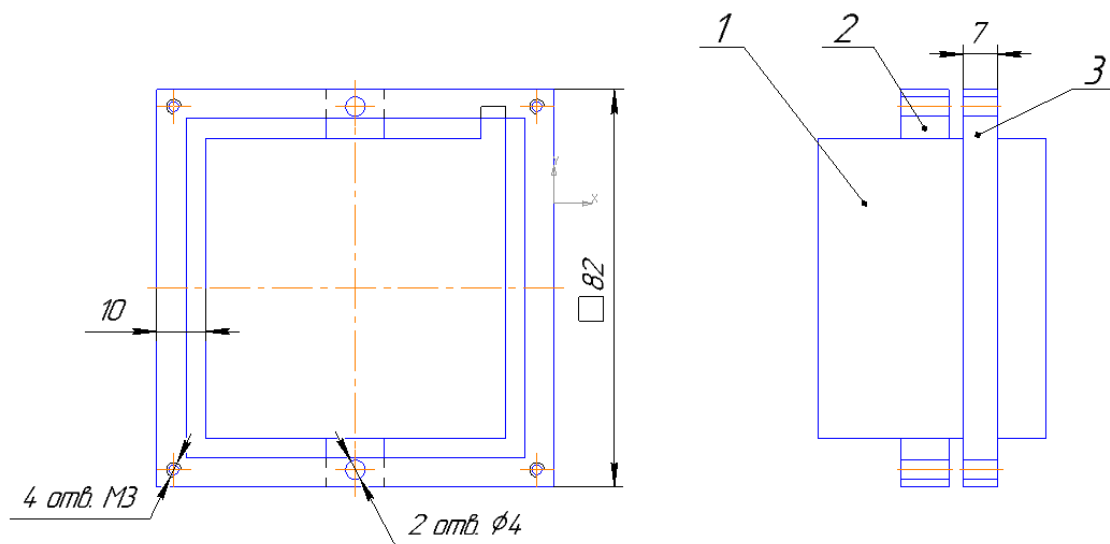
Установка О-образного сердечника трансформатора ТЛМ
